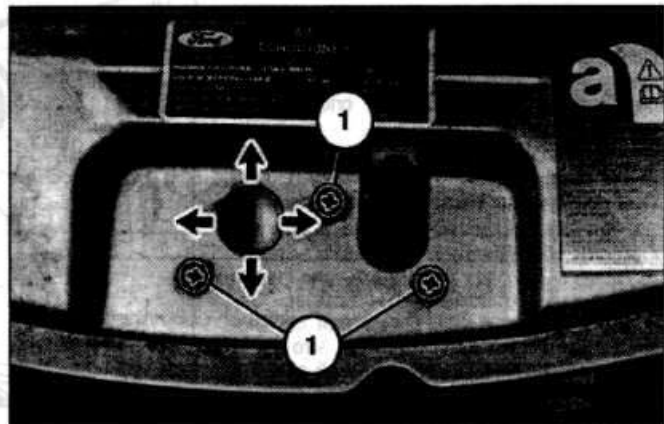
Вид болтов регулировки положения фиксатора замка капота
